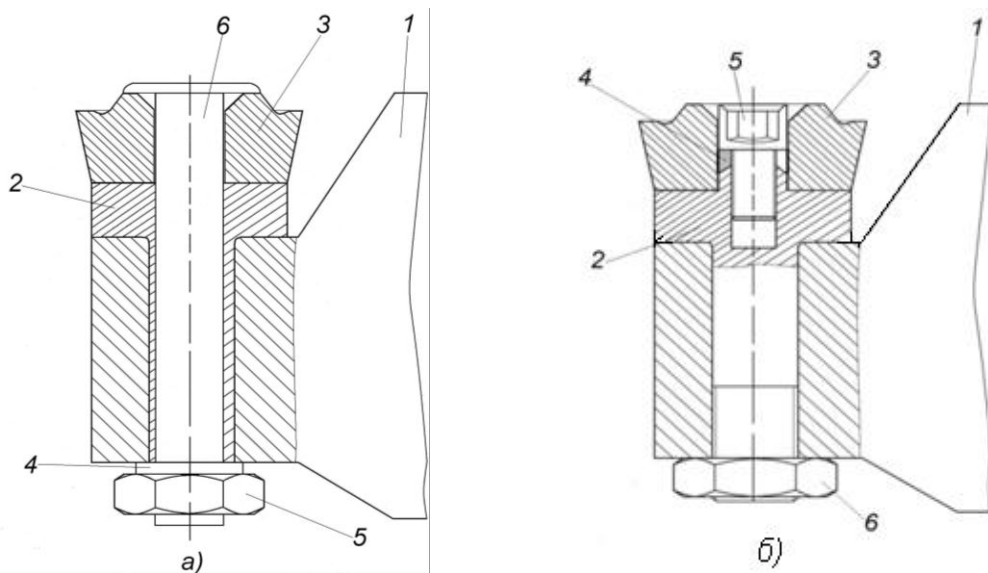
Базовая (а) и усовершенствованная (б) конструкции сборного чашечного резца
